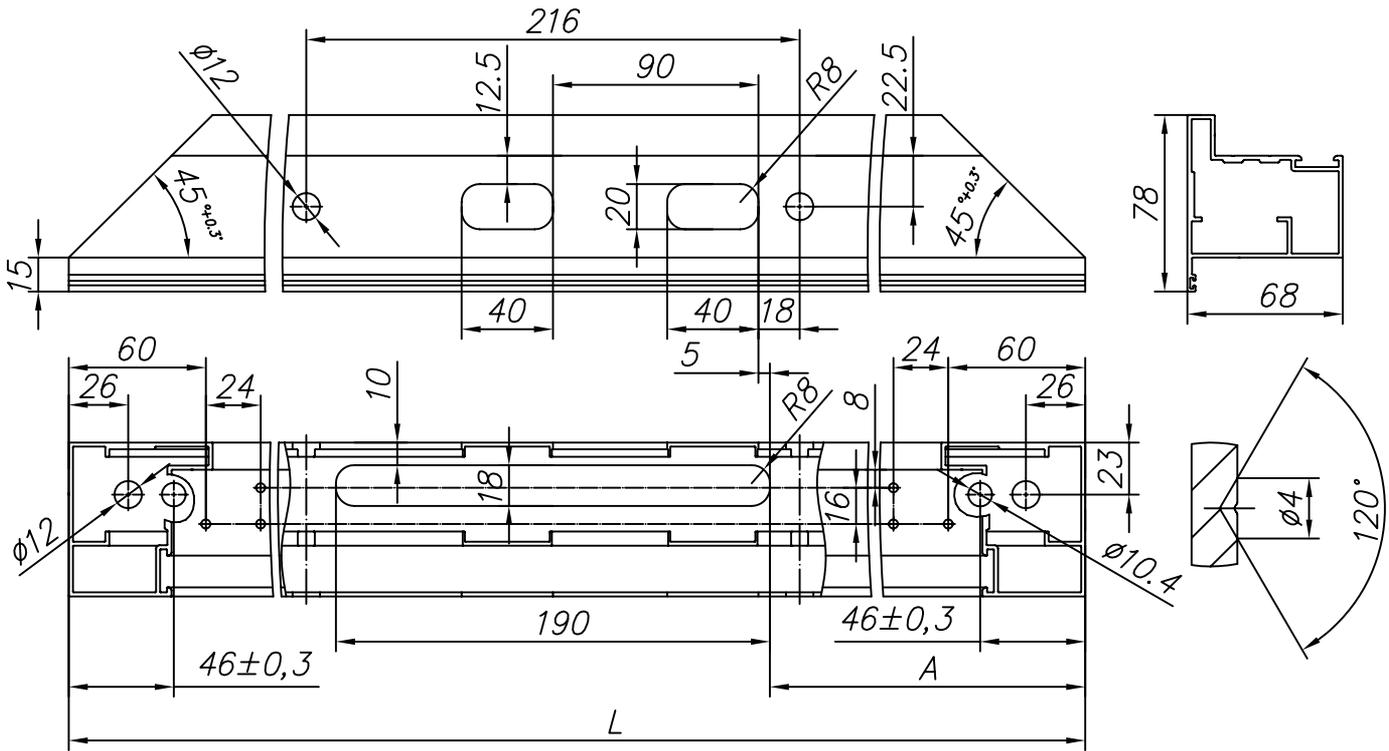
Изготовление стойки с пазом для замка из профиля FLGU 400.0108 (открытие наружу, влево)
